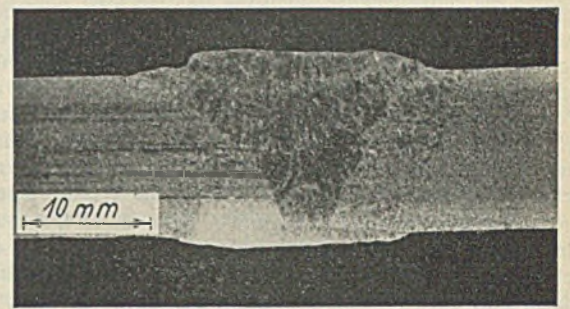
Gasschmelzschweißung, V-Naht.
